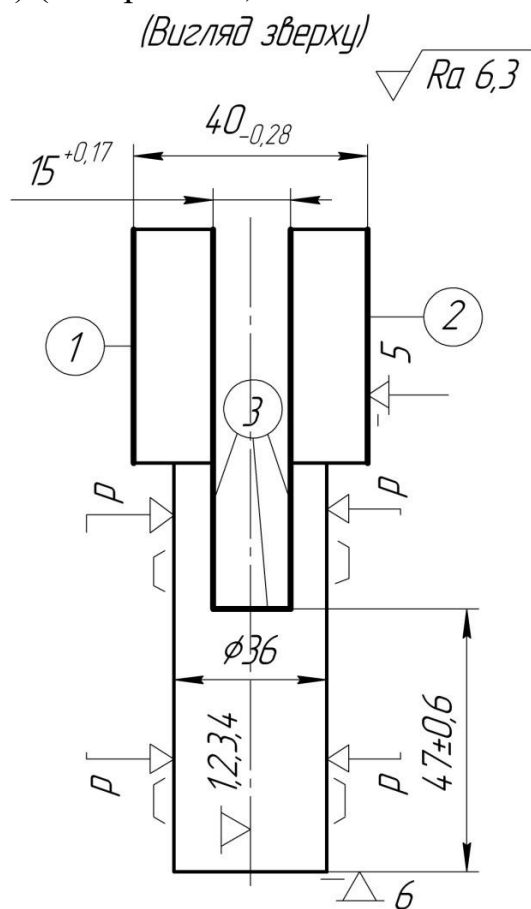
Схема базування та ескіз обробки торців, вушок і паза
